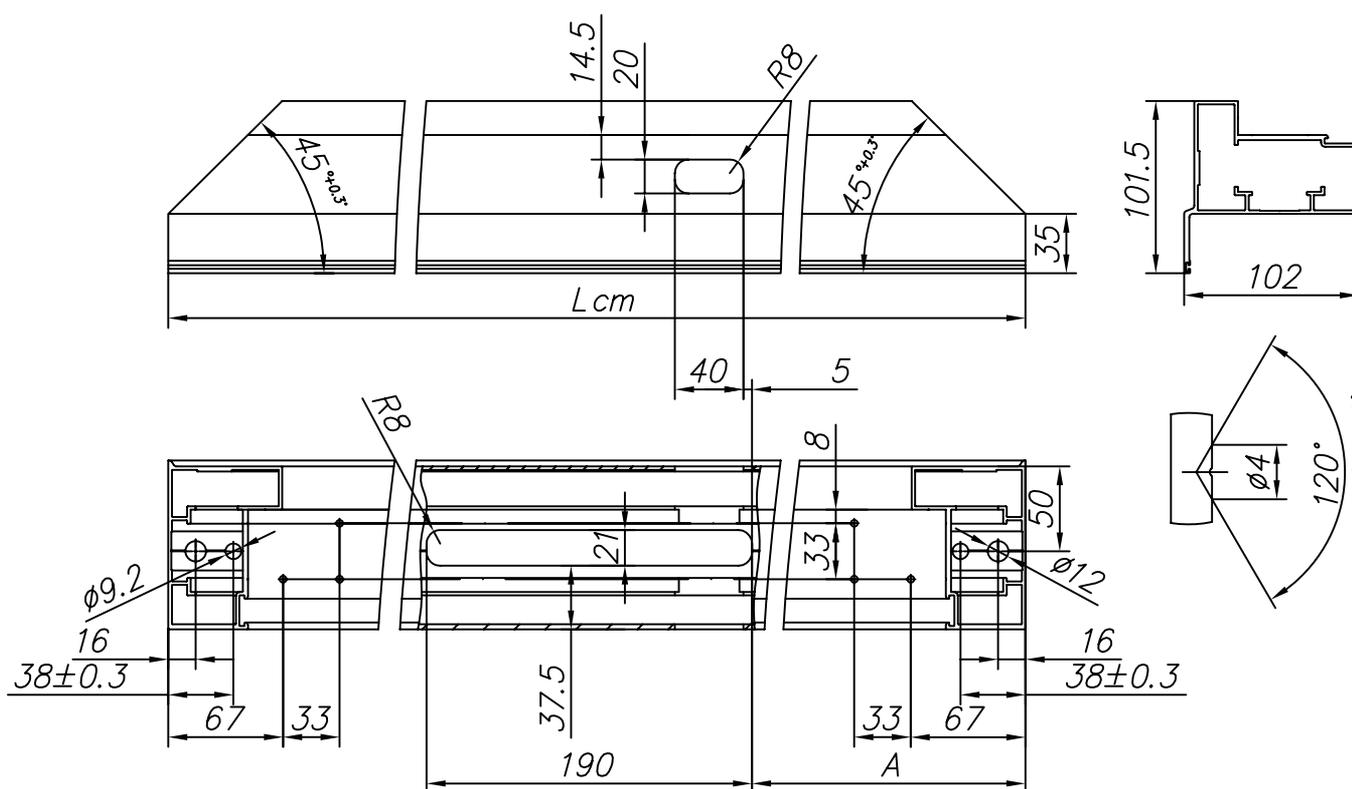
Изготовление стойки FLGU.400.0116 с пазом для замка FLGU.400.1012
